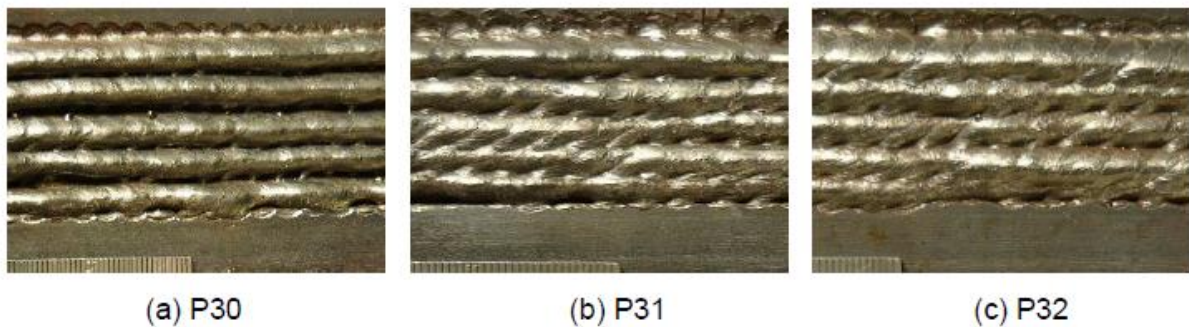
Aspecto superficial do revestimento soldado no MIG/MAG convencional
